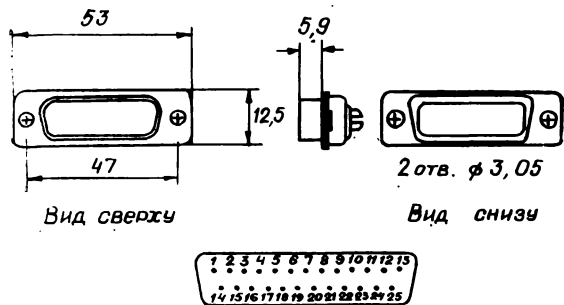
Габаритные размеры миниатюрного соединителя типа D, предлагаемого в качестве стандартного для параллельного видеостыка
